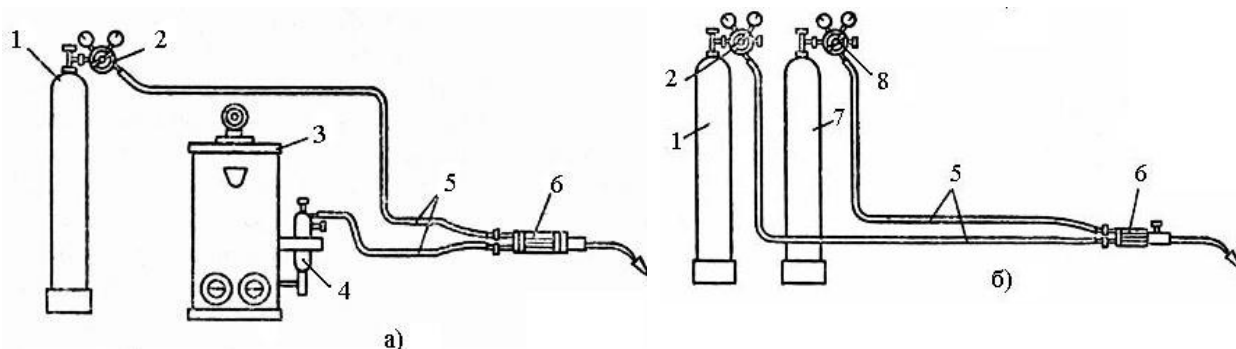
Схема газопитания передвижного сварочного поста:
